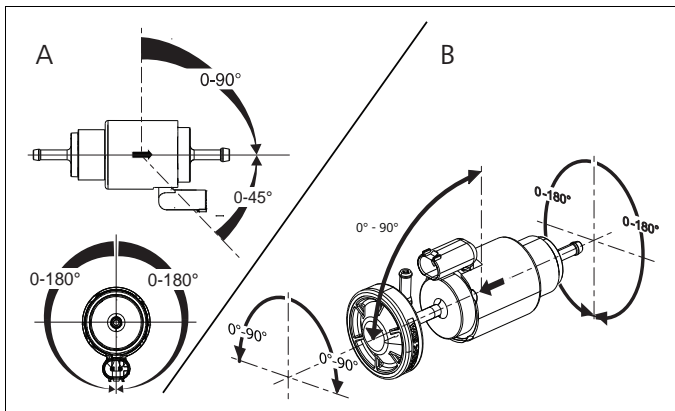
Einbaulage Brennstoffpumpe DP 42
